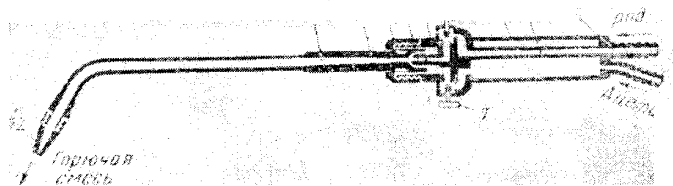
Инжекторная сварочная горелка
